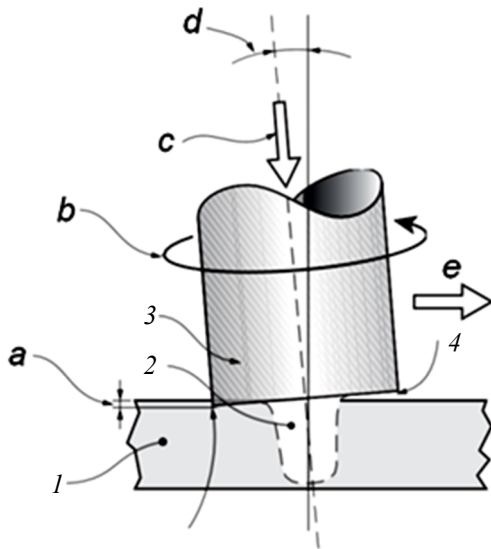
Схема сварки трением с перемешиванием стыкового соединения:
